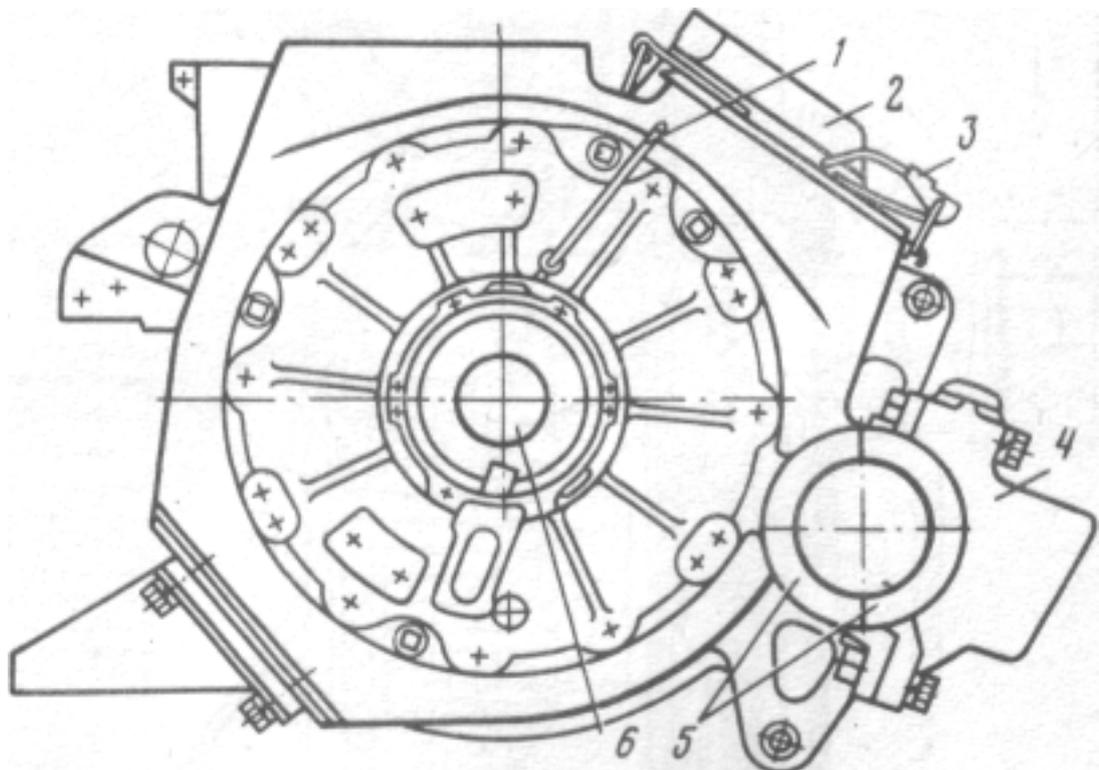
Общий вид тягового двигателя НБ-418К6 :
